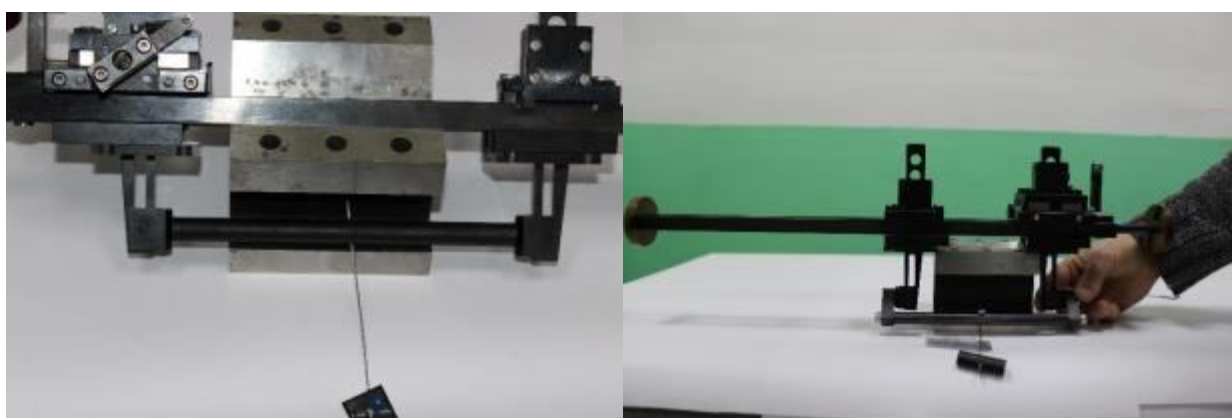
Типовые конструкции индикаторных приборов с КЭ ИН типа «ролик»
